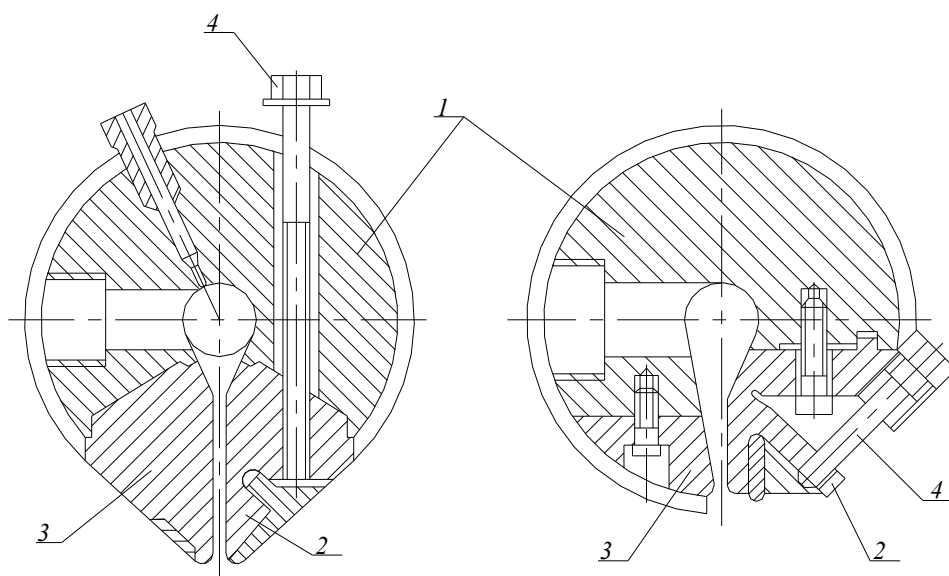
Головки для виробництва тонких плівок: 1 – корпус, 2 – верхня регульована губка, 3 – нерухома губка, 4 – регулювальний болт
